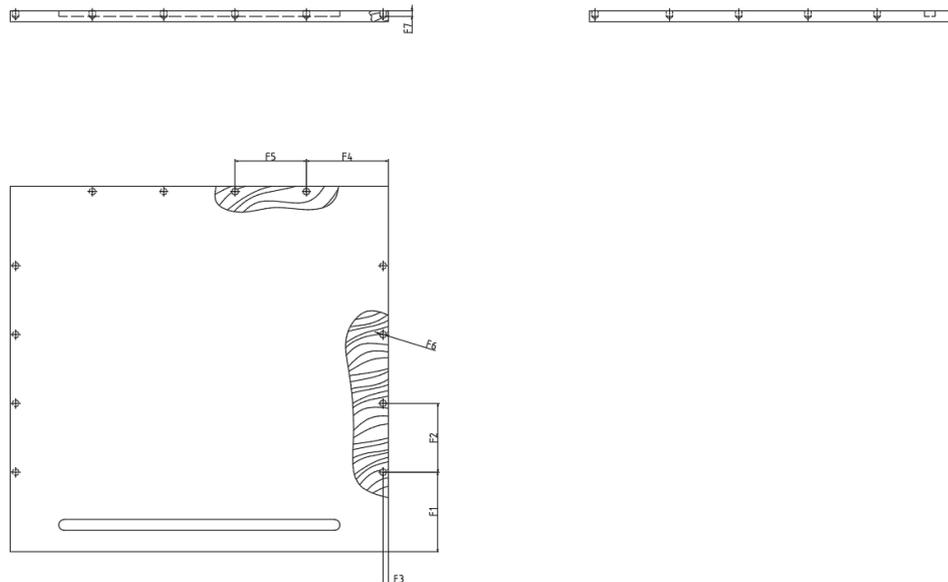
Plano Dimensionado Previo de la Tapa Cajón 2.1.1.1
